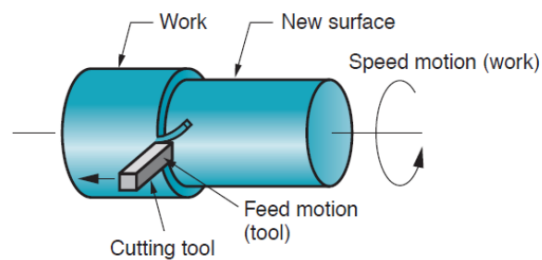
เครื่องกลึงซีเอ็นซี (CNC Turning Machine)
